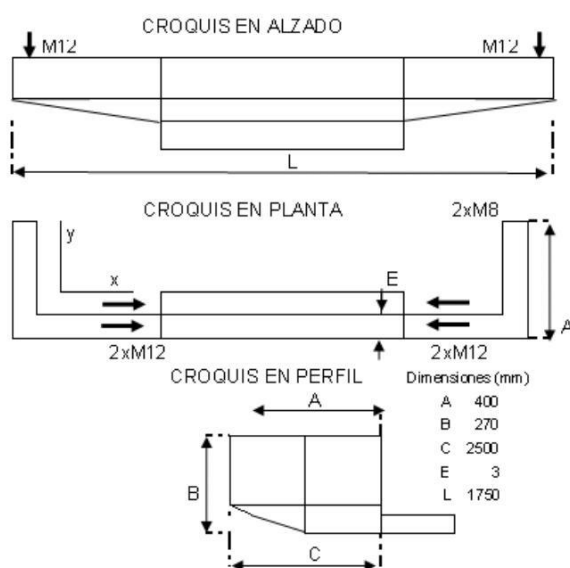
Alçat, planta i perfil del para-xocs davanter reformat
